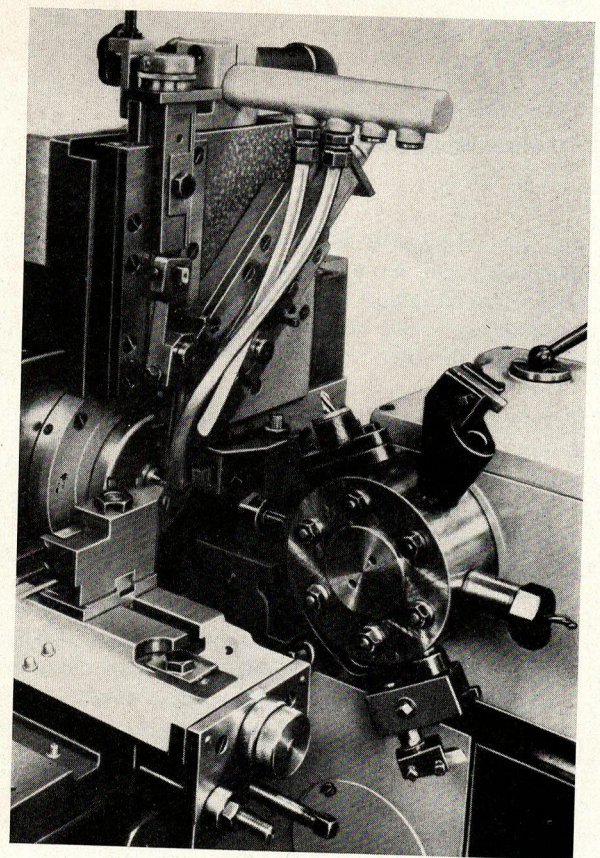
Arbeitsraum des Drehautomaten mit bestückten Werkzeugschlitten
